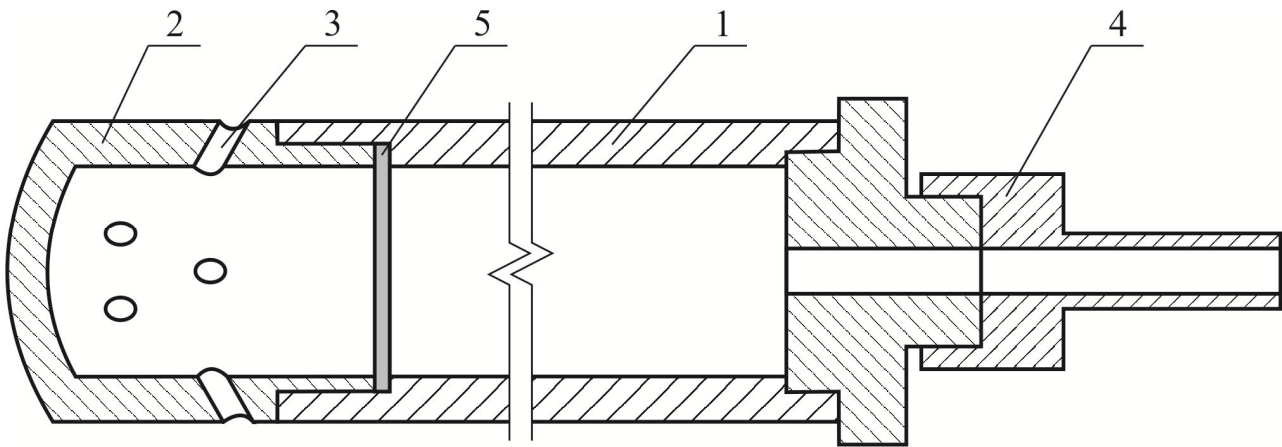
Конструкція патрона аеродокс: 1 – порожній сталевий циліндр; 2 – розрядна голівка; 3 – вихлопні вікна; 4 – штуцер; 5 – запірний диск
